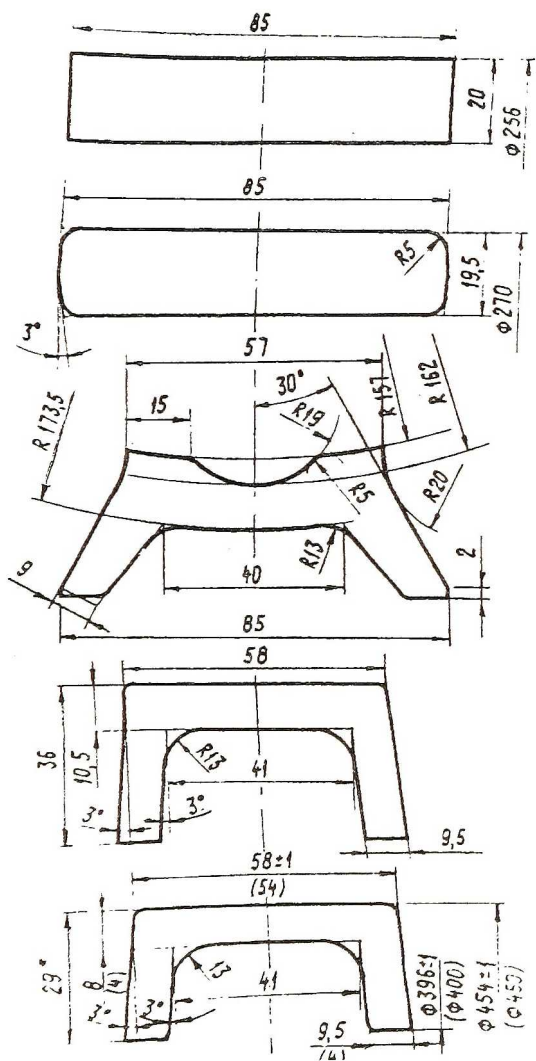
Калибровка заготовки промежуточного кольца дисков из сплава ХН68ВМТЮК-ВД
